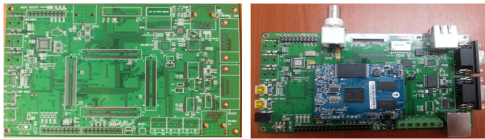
해양 네비게이션 PCB 및 완성모듈
